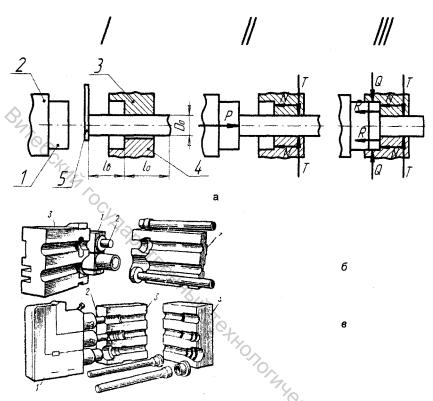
Штамповка на ГКМ: a - схема процесса штамповки; б – двухручьевой штамп; в – трехручьевой штамп
